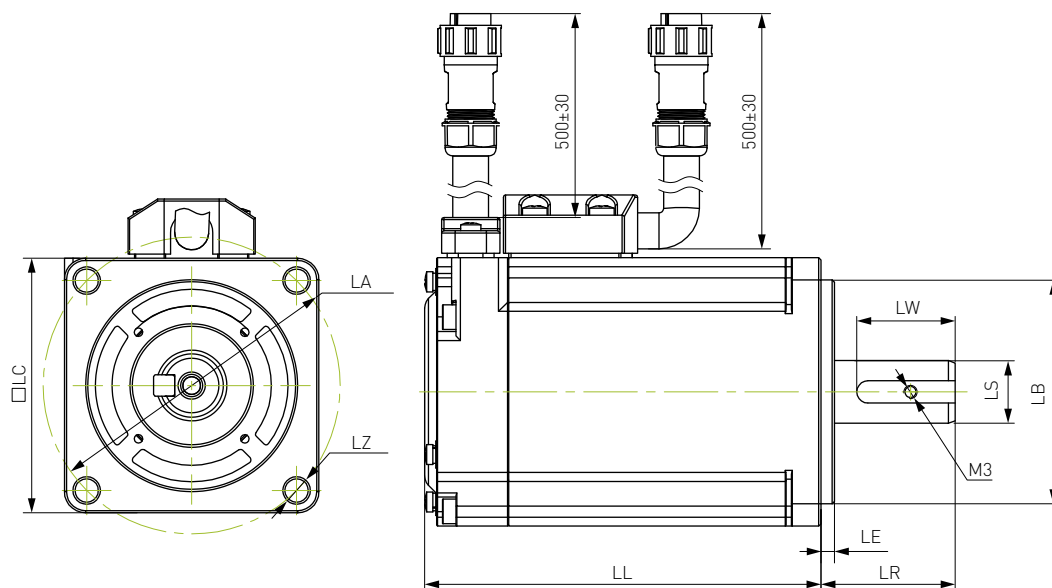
Габаритный чертеж серводвигателя без тормоза (мм).
